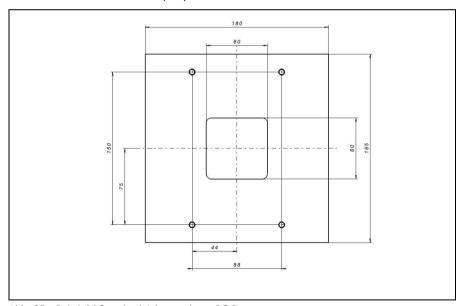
Bohrbild Standard-Adapterplatte BG D
